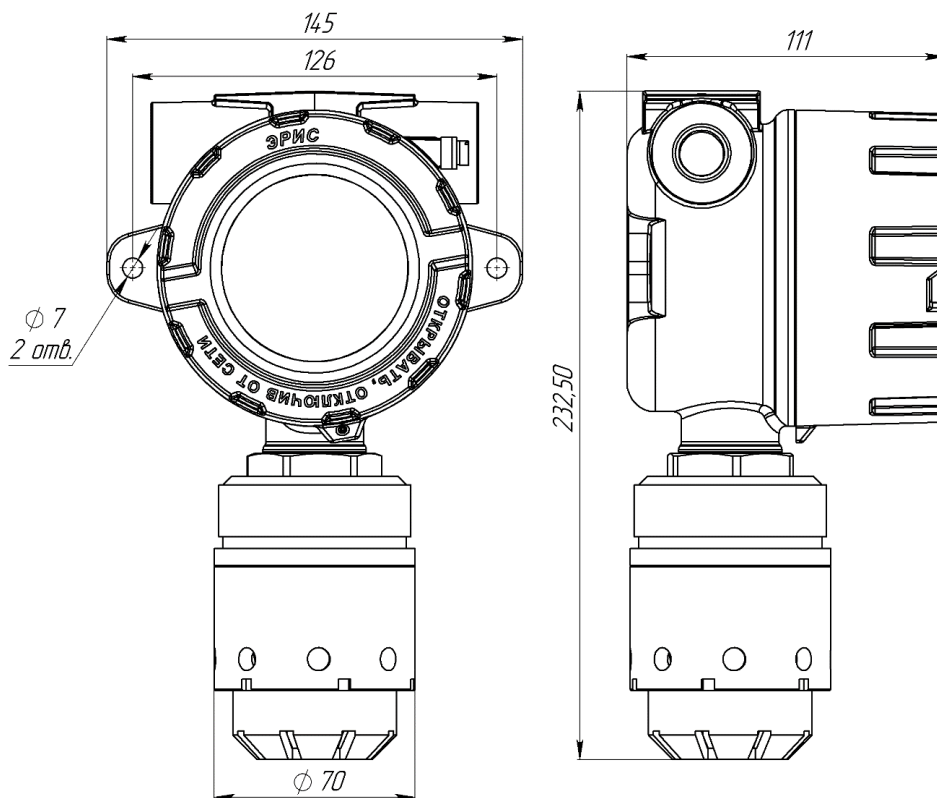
Габаритные размеры газоанализатора в корпусе типа А
